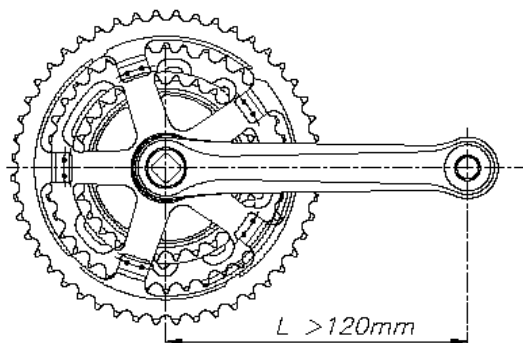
Dimensões de pedivela montada com engrenagem de bicicleta de uso adulto.
